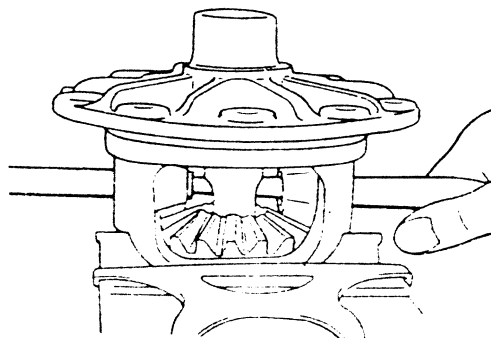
(b) 用推杆拆卸差速小齿轮轴
